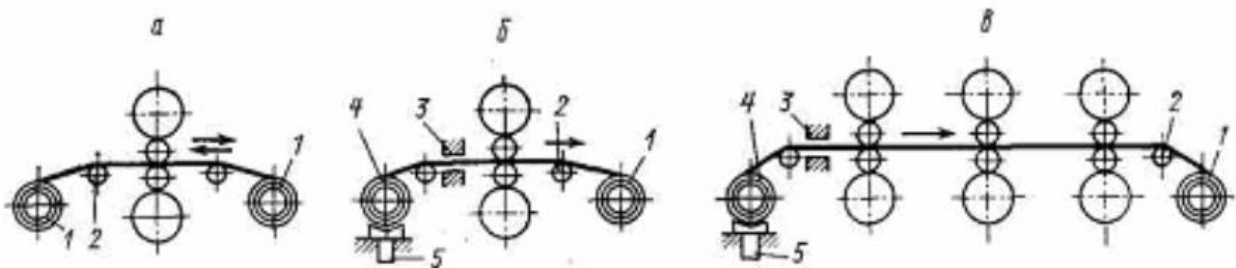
Схема розташування барабанних моталок на станах холодної прокатки смуги: а - реверсивному; б – нереверсивному одноклітинний; в - безперервному багатоклітинному; 1 - моталки; 2 - напрямні холости ролики; 3 - притискний стіл з проводками; 4 - розмотувач; 5 - гідроциліндр
